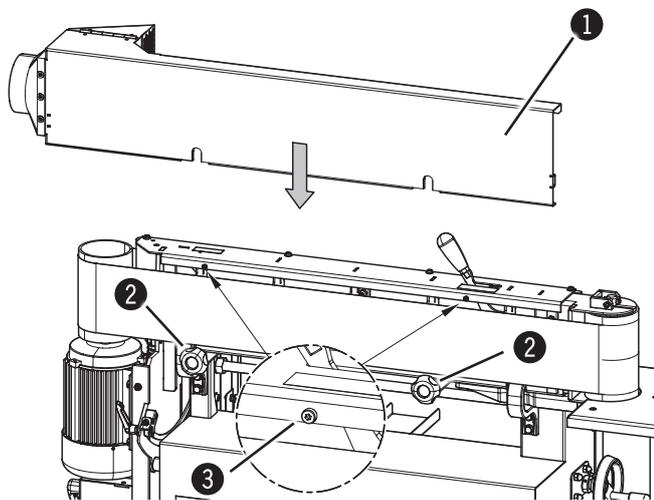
Montaje - Cubierta trasera de la banda de lijado
